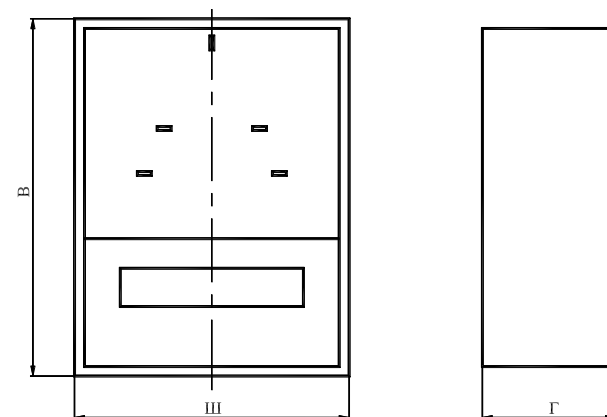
Габаритные размеры корпусов металлических ЩУРН
